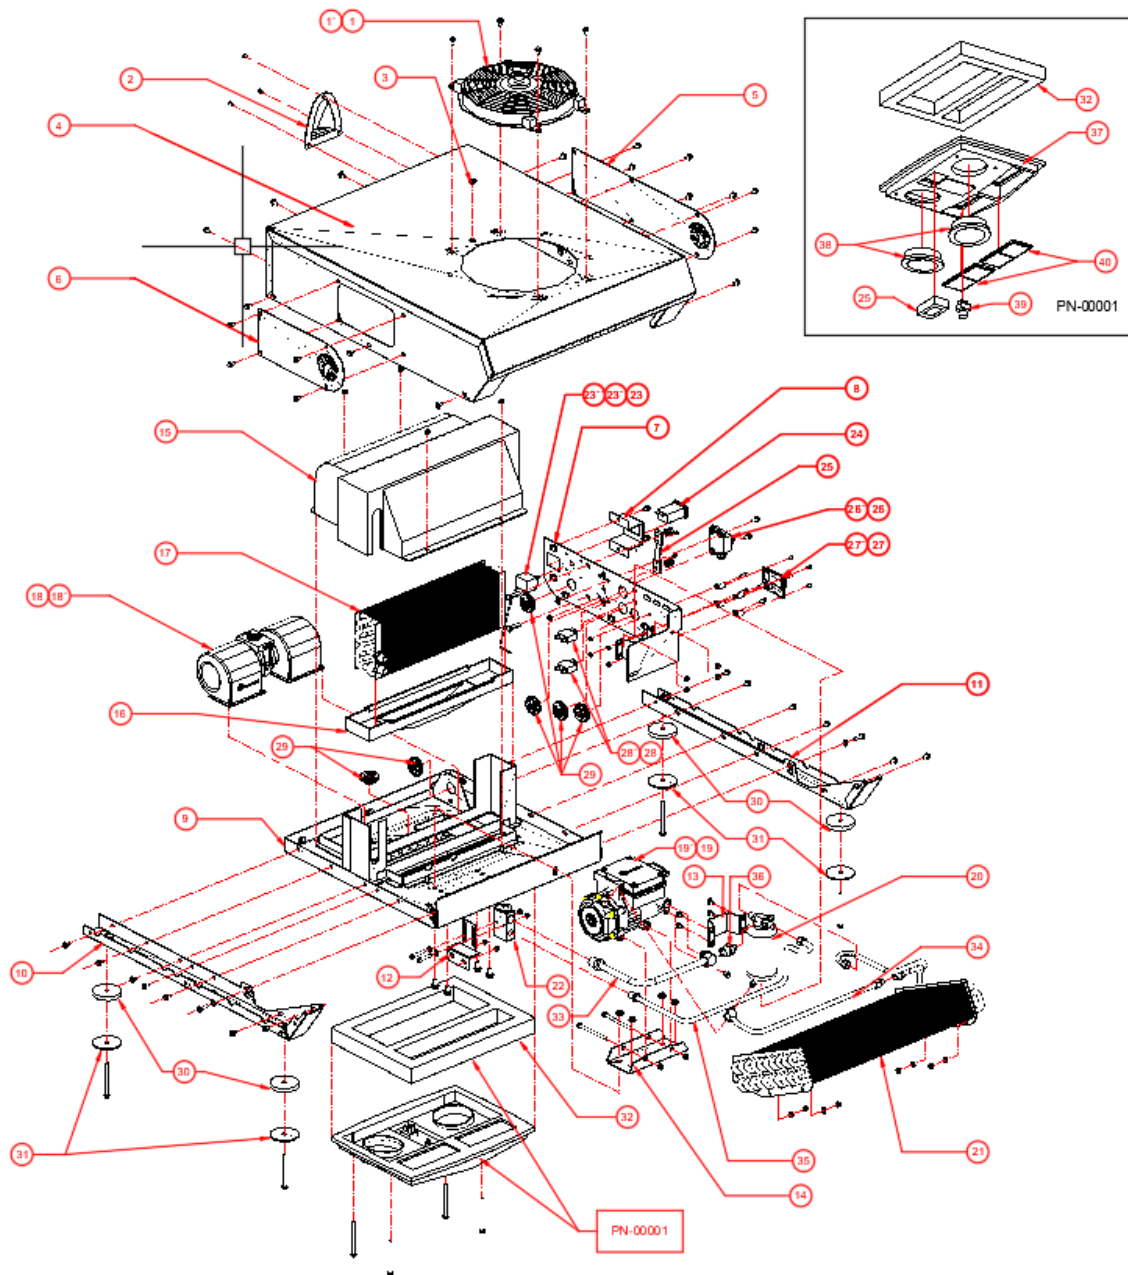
Disposición de Componentes - Diagrama de Vista Explosionada
